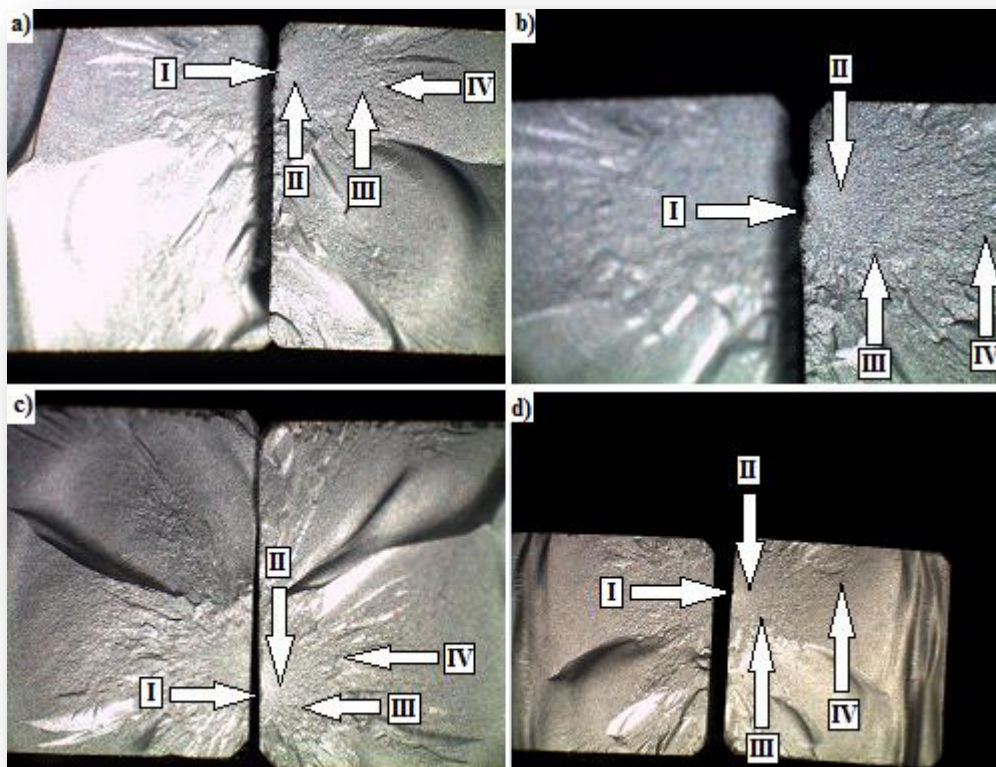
Superfícies de fractura dos provetes maquinados a partir do bloco WF40: a) e b) com programa de desbaste; c) e d) com programa de acabamento. São ainda mais ou menos identificáveis as seguintes zonas: I - de origem da fractura; II - espelhada (zona de fractura lenta); III - mista; IV - propagação de fissura frágil.
